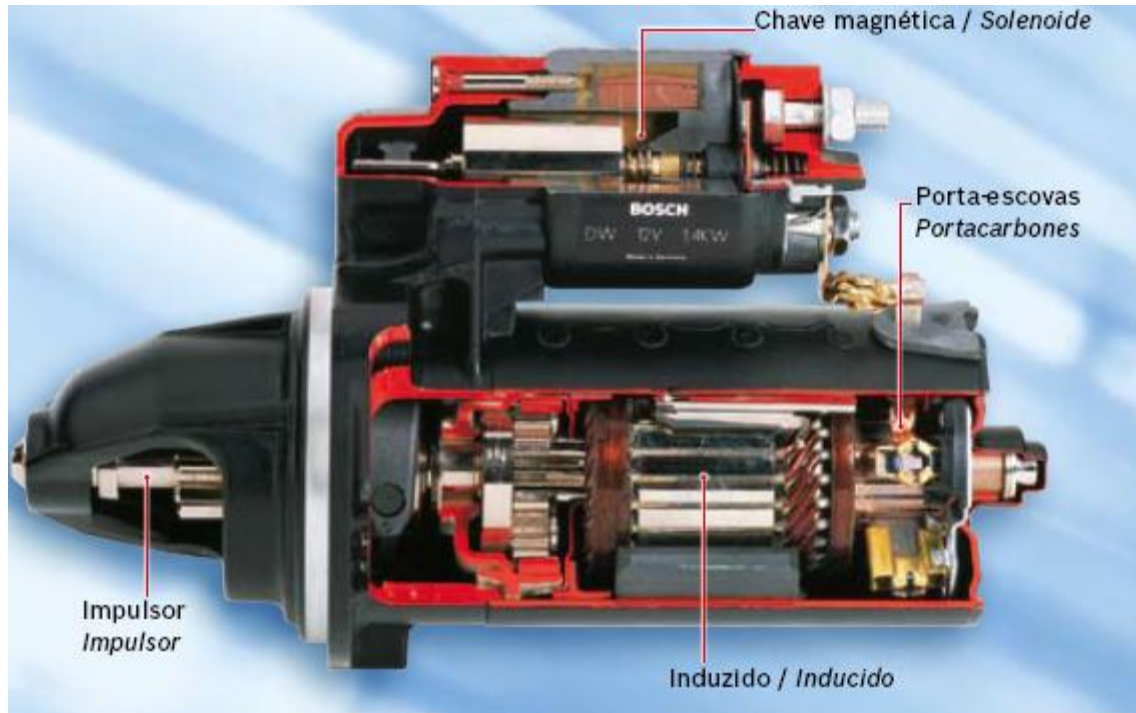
Motor atual de partida Bosch e seus componentes internos.
